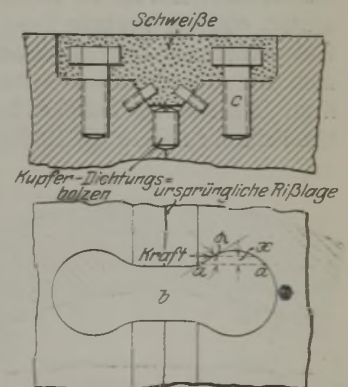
Kopfankeerschweißung für Zylinderschweißungen.
